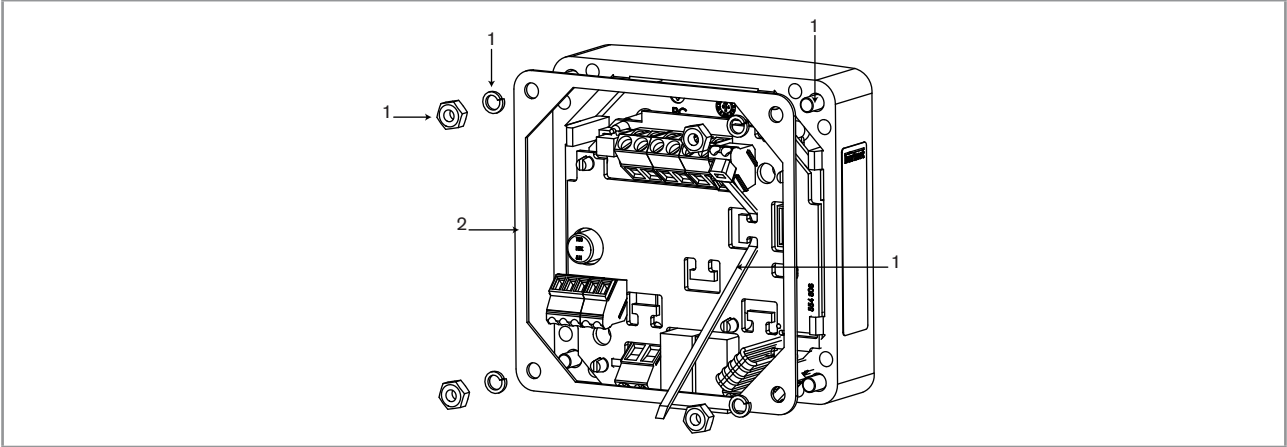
Explosionszeichnung der Ersatzteile des Durchflusstransmitter 8025 in Schaltschrankmontage-Ausführung
